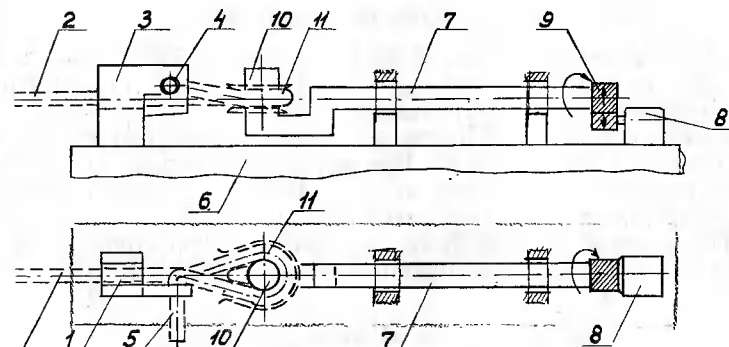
Приспособление для изготовления петель звеньевых струн: 1 — желоб; 2 — звеньевая струна; 3 — упор; 4 — отверстие для струны; 5 — конец струны; 6 — основание; 7 — стержень; 8 — привод (ручной или электродвигатель); 9 — редуктор; 10 — валик; 11 — коуш
